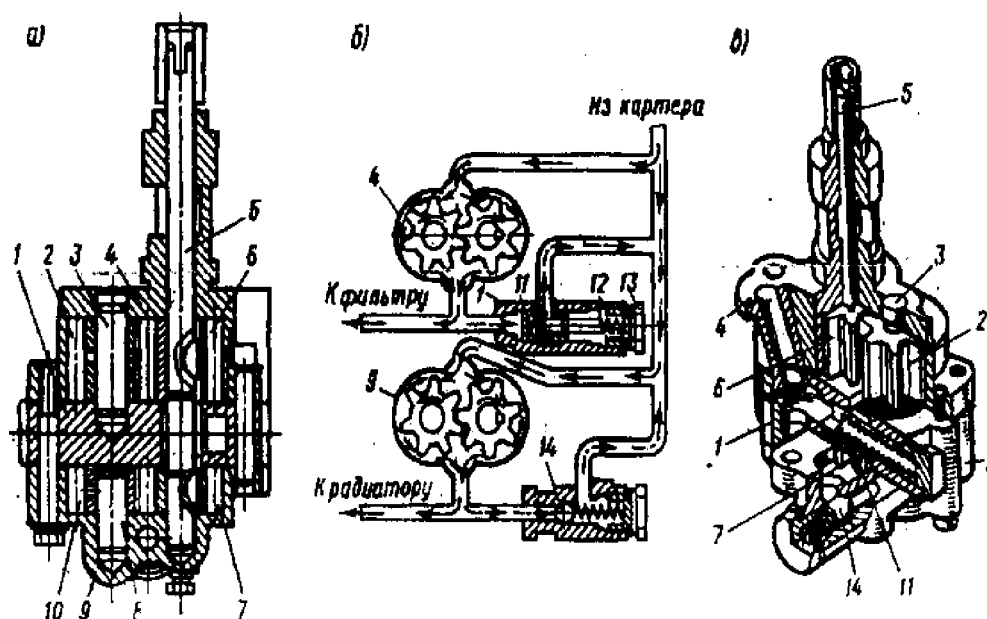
Двухсекционный смазочный насос: а – продольный разрез; б – схема работы; в – общий вид
